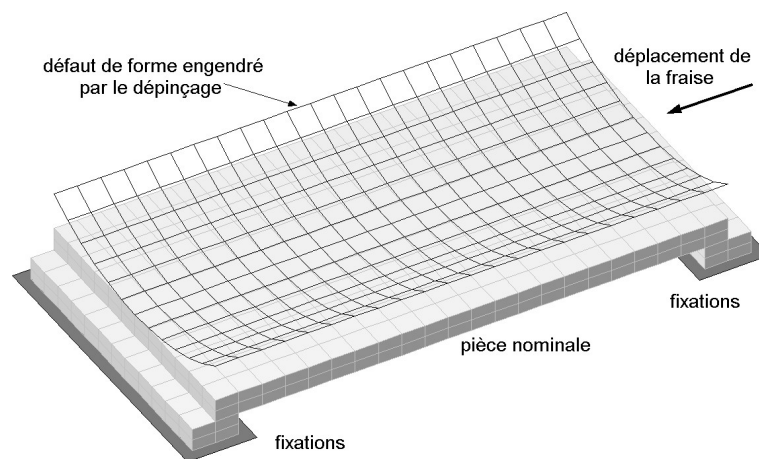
défaut de forme engendré par le dépinçage de la fraise
